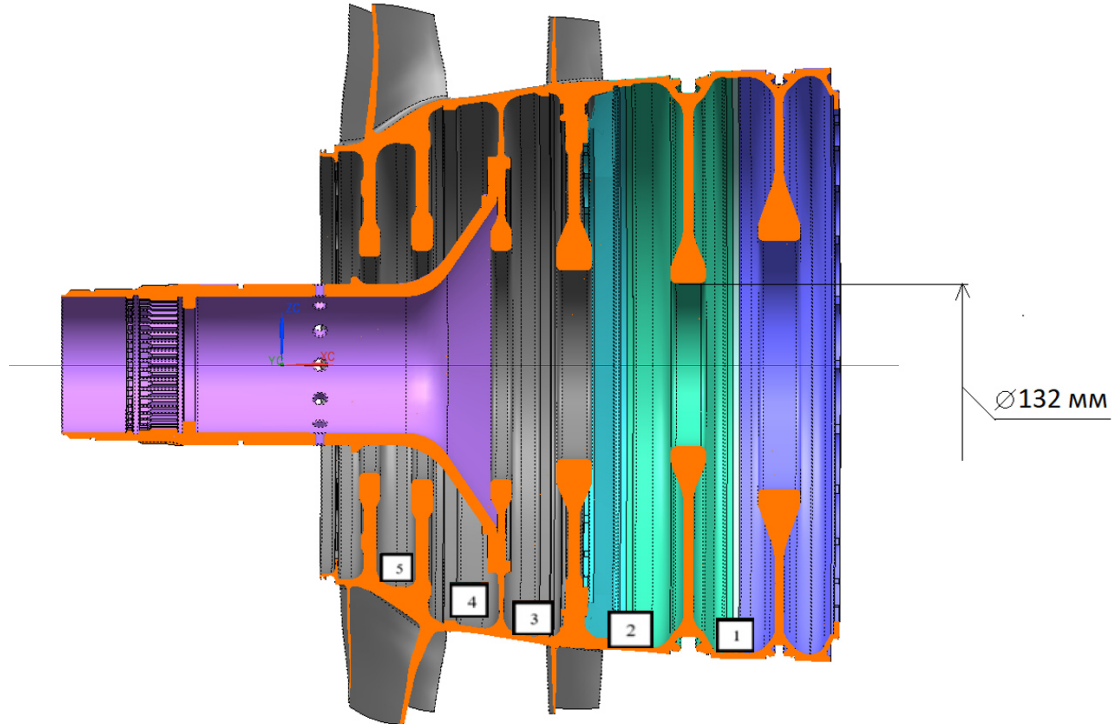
Барабан 1...4 ст. КВД двигателя ПД-14 с приклеенными образцами
